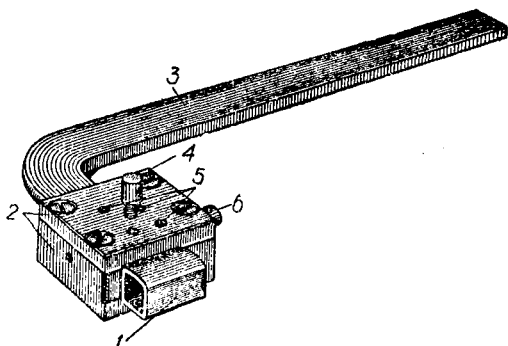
Кондуктор для сверления отверстий в угольнике и ушке:
